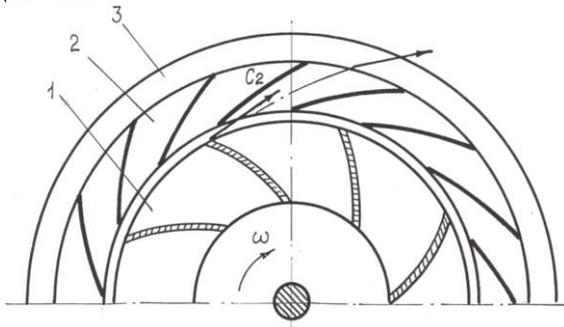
Корпус центробежного компрессора в разрезе: 1- рабочее колесо; 2- лопаточный диффузор; 3- безлопаточный диффузор
